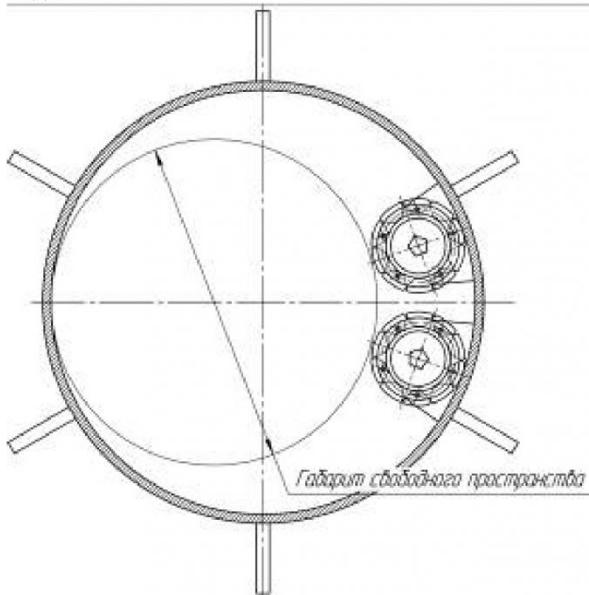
Схема гидропривода геохода с двумя гидромоторами
